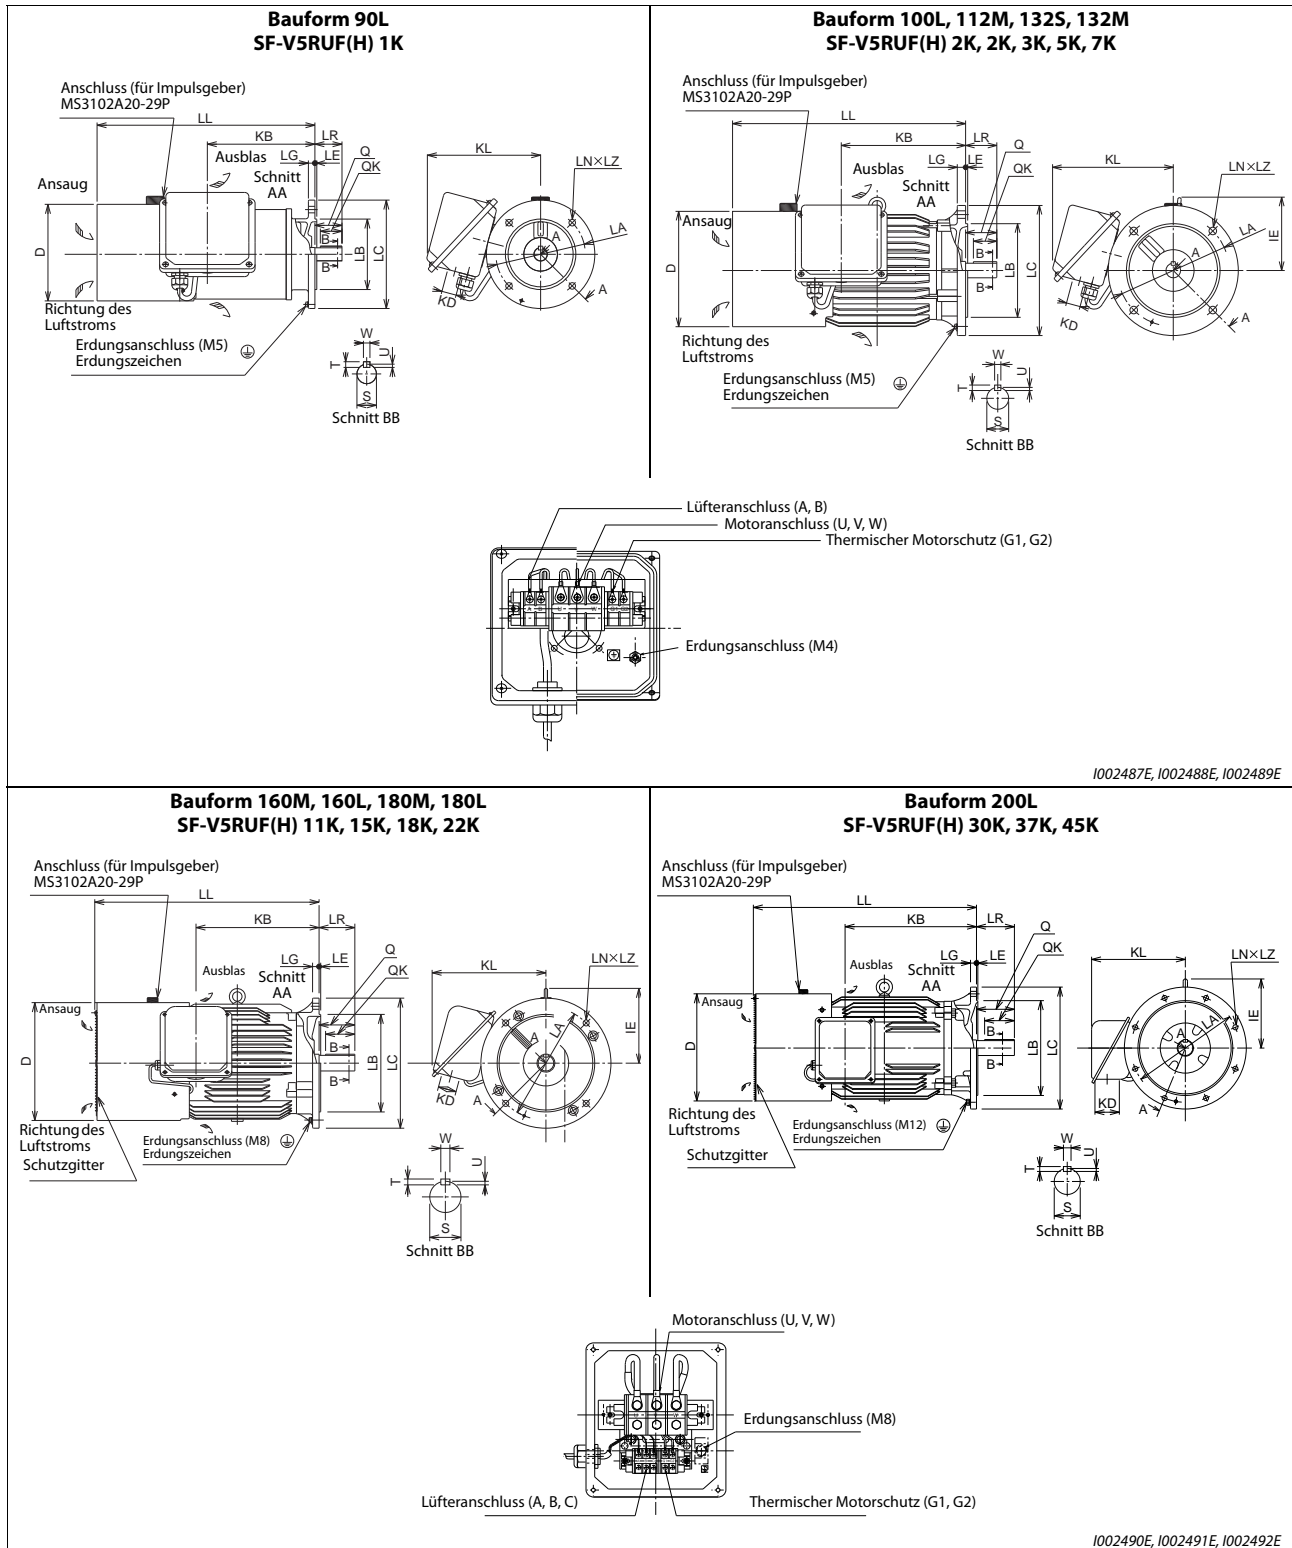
Maßzeichnungen der Motoren SF-V5RUF(H) (mit Befestigungsflansch)
